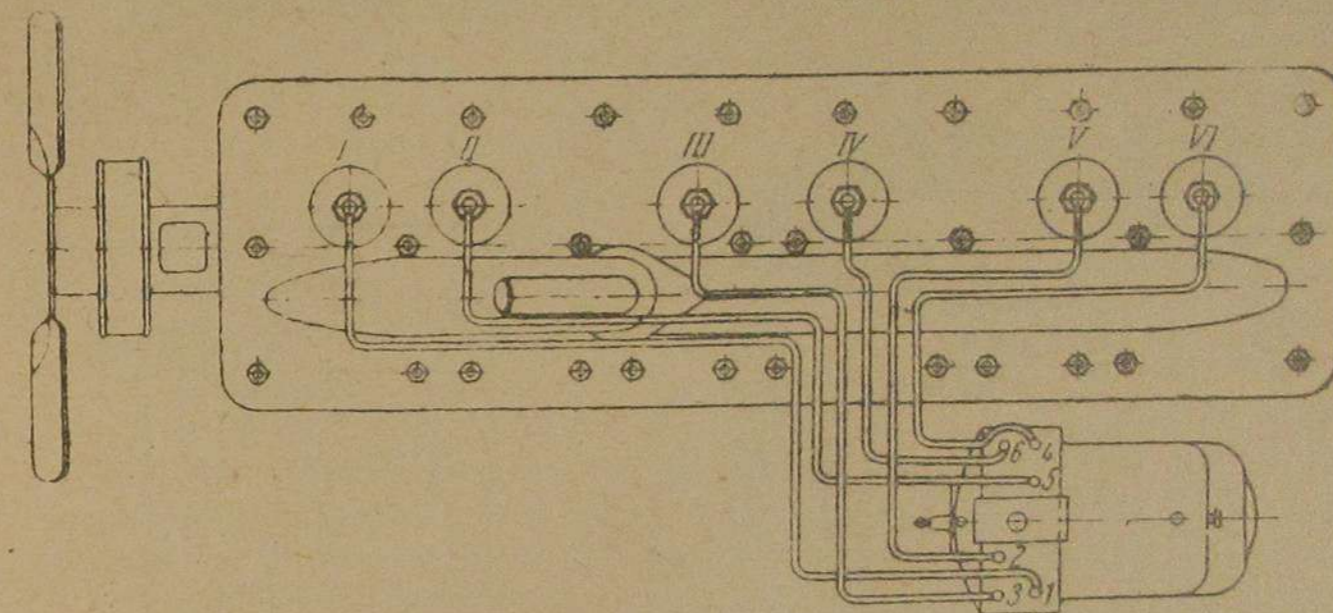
Порядок присоединения проводов к свечам. Римскими цифрами обозначены порядковые номера цилиндров
